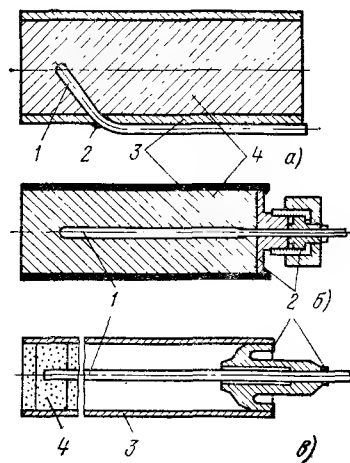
Установка ТЭП для измерения температуры топлива с уплотнением вывода в оболочке (а), с резьбовым уплотнением ТЭП (б), с уплотнением сваркой оболочки и ТЭП (в): 1 — ТЭП; 2 — уплотнение; 3 — оболочка; 4 — топливо
